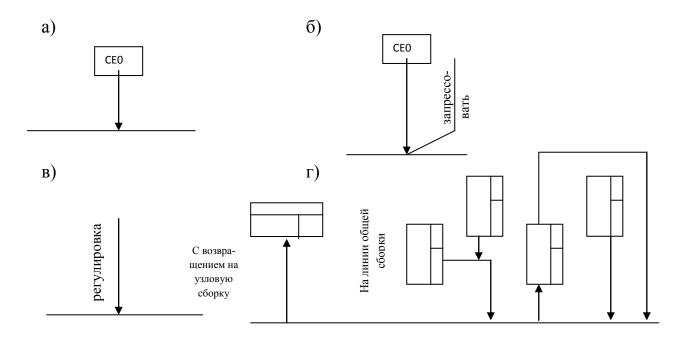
Формализационные обозначения сборочных действий в технологической схеме сборки
